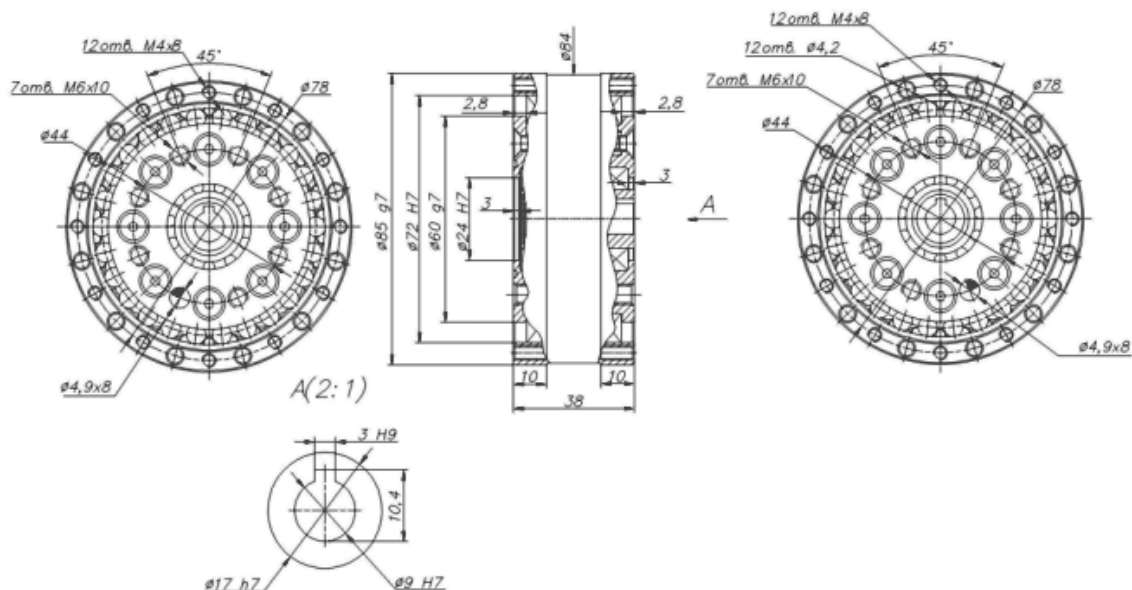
Габаритно-присоединительные размеры ПЦР 85-95А
